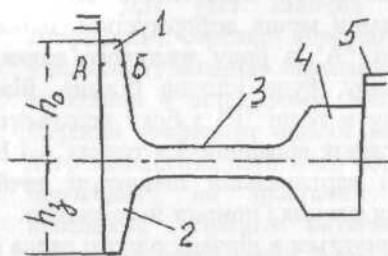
Рейковий калібр: 1 - відкритий фланець; 2 - закритий фланець; 3 - шийка; 4 - головка; 5 - проміжок між валками
